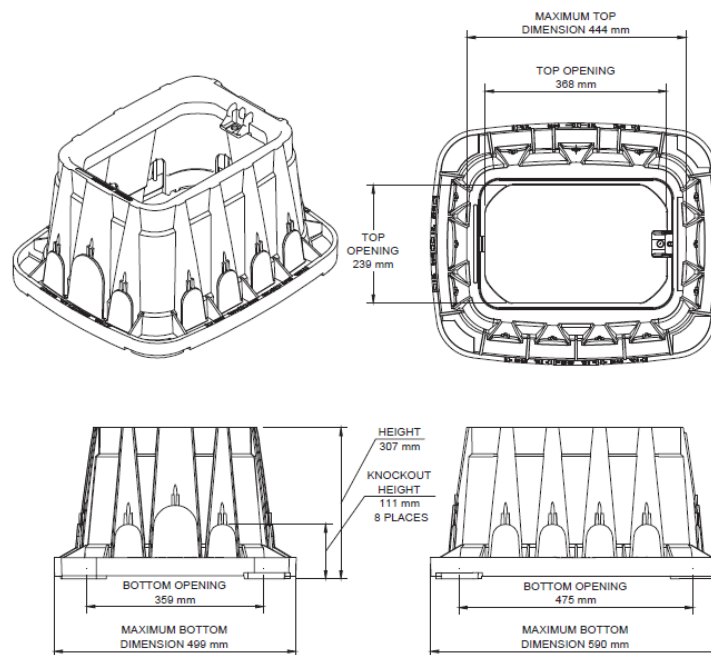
Detalle suministrado por el fabricante de una arqueta de riego tipo
